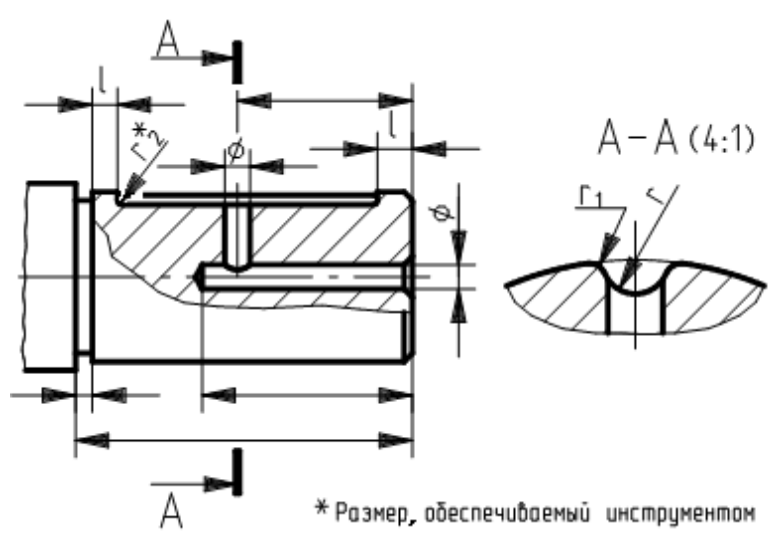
Нанесение размеров для смазочных отверстий и канавок
